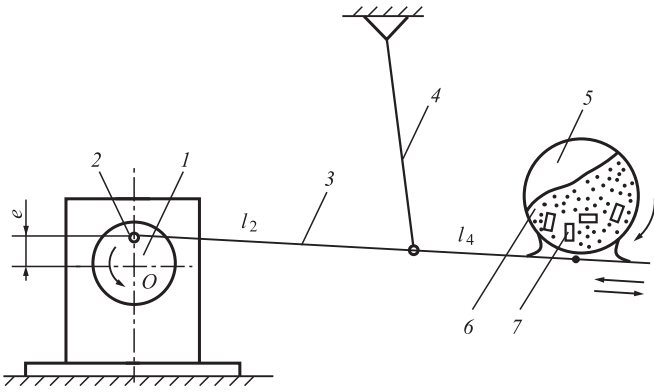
Схема станка с шарнирно-рычажным приводом: 1 — эксцентриковый диск; 2 — ведущий палец; 3 — траверса; 4 — подвеска; 5 — рабочая камера; 6 — абразивная среда; 7 — обрабатываемые заготовки
